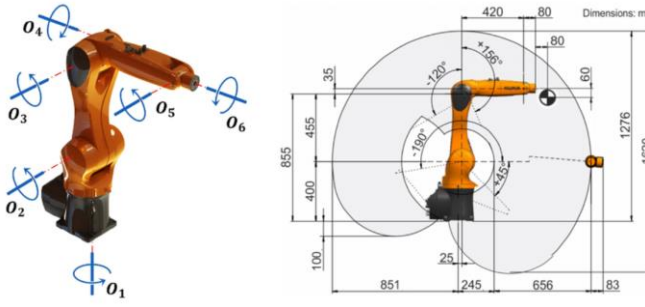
Cadena cinemática y dimensiones principales del robot KUKA KR6 R900 SIXX
